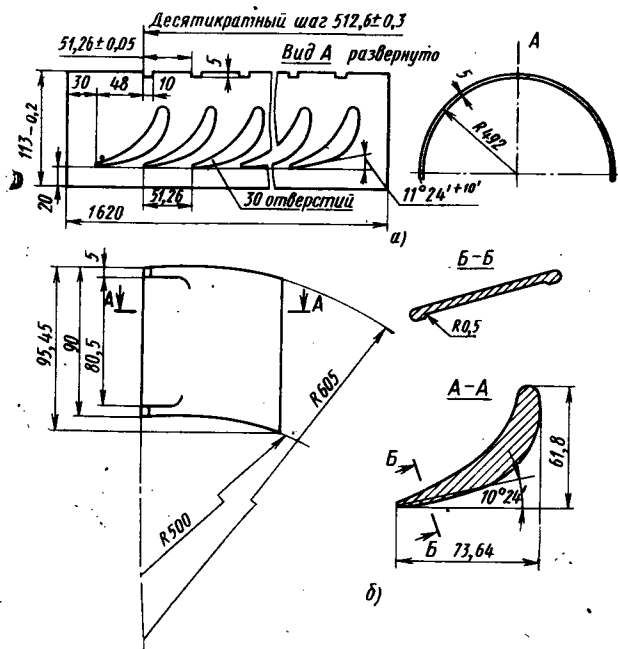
Бандаж цилиндрической формы рабочего аппарата для сварной диафрагмы (а) и направляющая лопатка диафрагмы (б)
